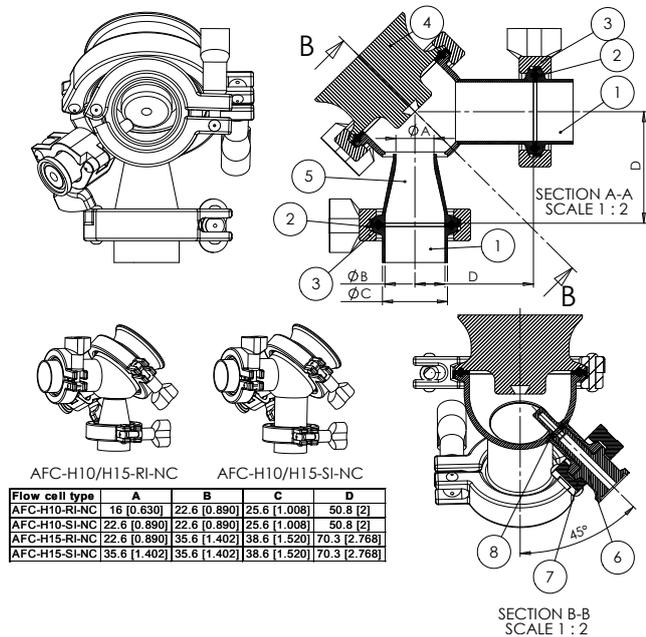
Montagem com virola sanitária, diâmetro do tubo 3" (80 mm) ou superior
